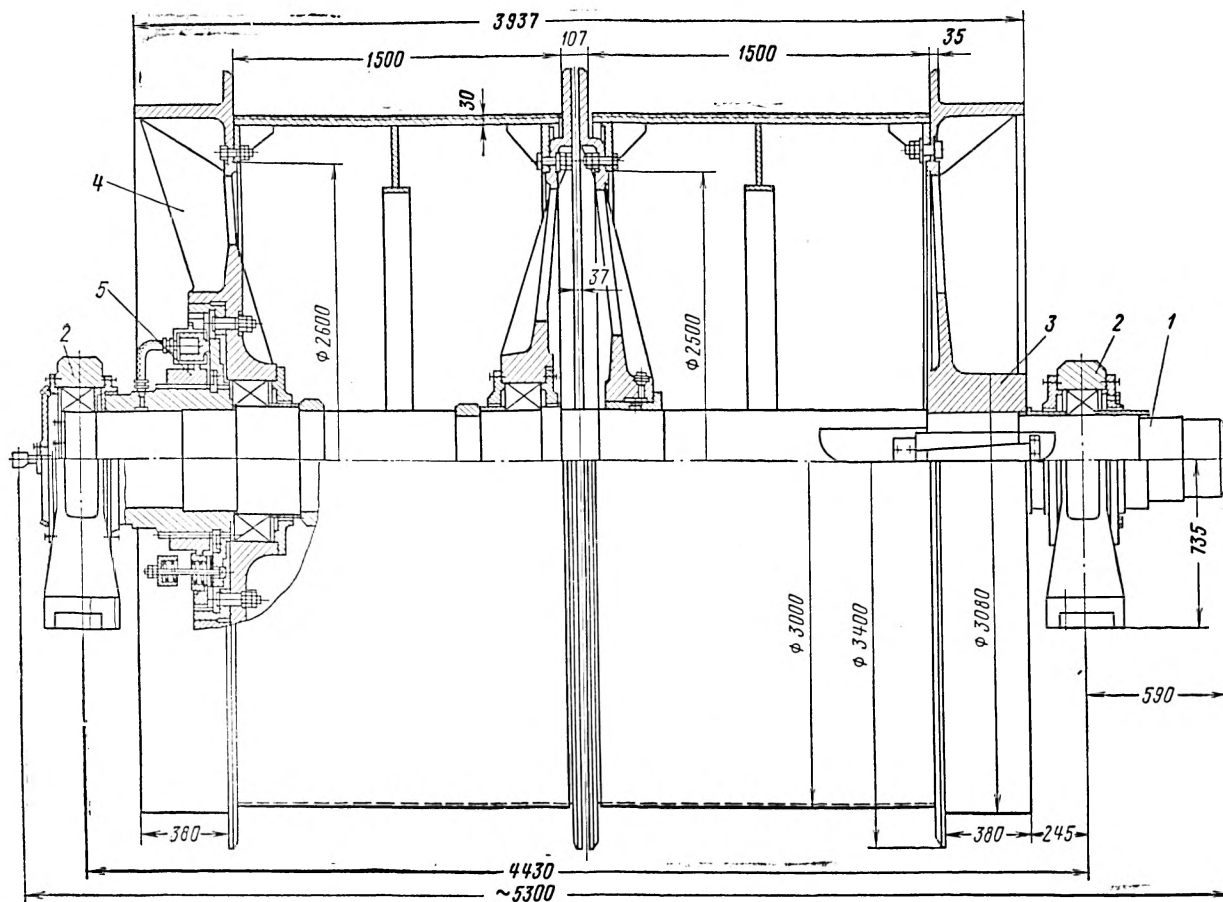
Сборка главного вала машины 2×3×1,5У:
